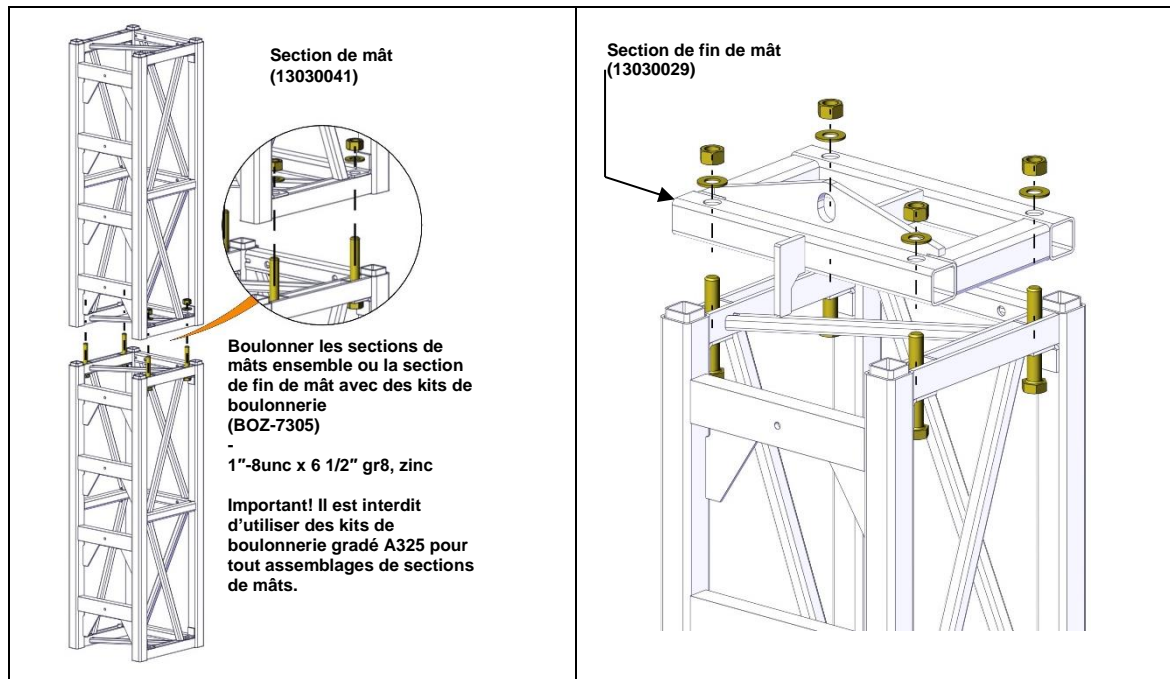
Boulonnage des sections de mât et section de fin de mât
